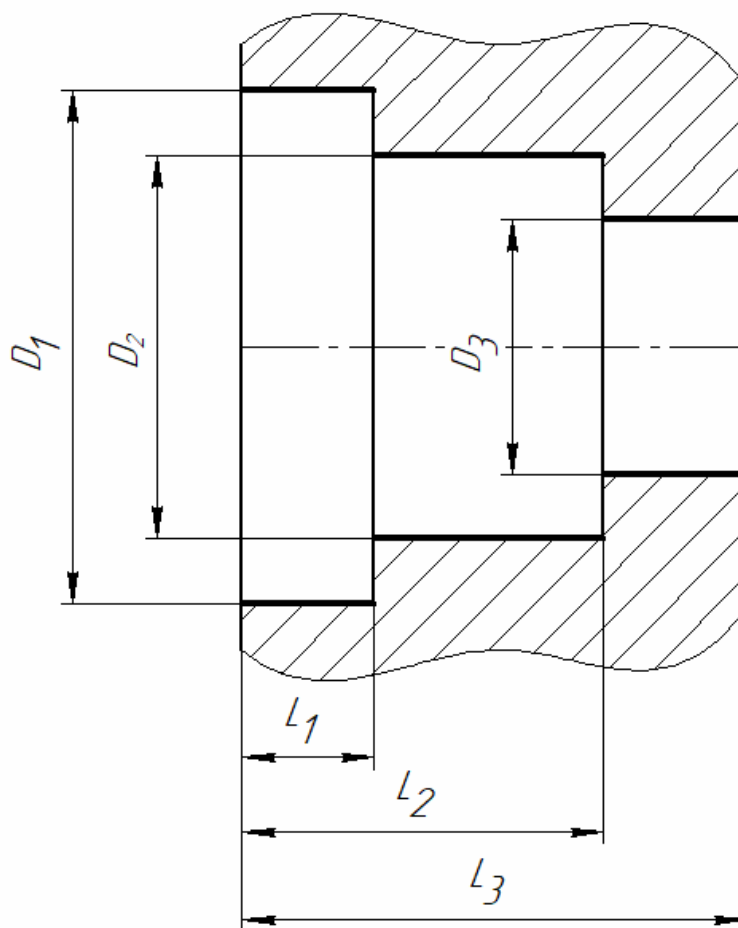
Схема типового ступенчатого отверстия, подлежащего обработке на станке с ЧПУ
